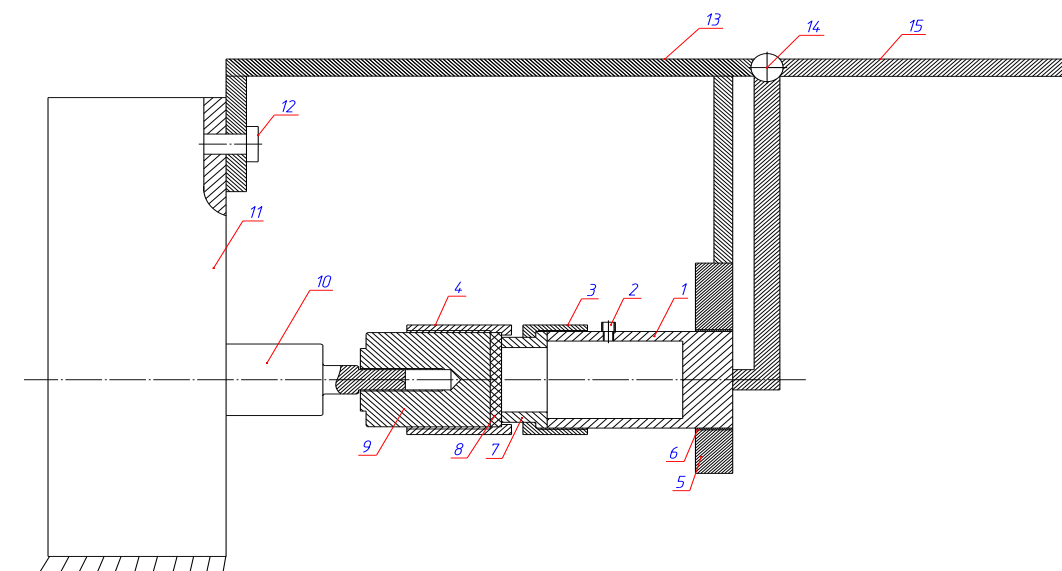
Схема приспособления для триботехнических испытаний резин методом торцевого трения: 1 – стакан, 2 – штуцер, 3 – крышка стакана, 4 – крышка цилиндра, 5, 13 – детали корпуса, 6 – бронзовая втулка, 7 – сменное кольцо, 8 – резиновое уплотнение, 9 – цилиндр, 10 – вал, 11 – машина трения СМТ – 1, 12 – болт крепежа, 14 – шарнир, 15 – рычаг нагружения
